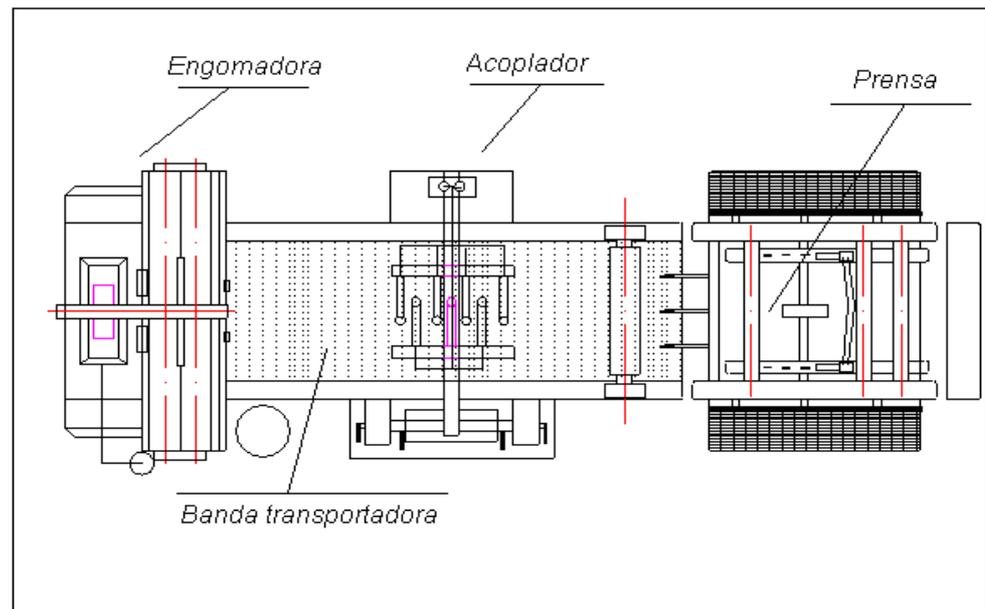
PLANO DE MÁQUINA CRATHERN
